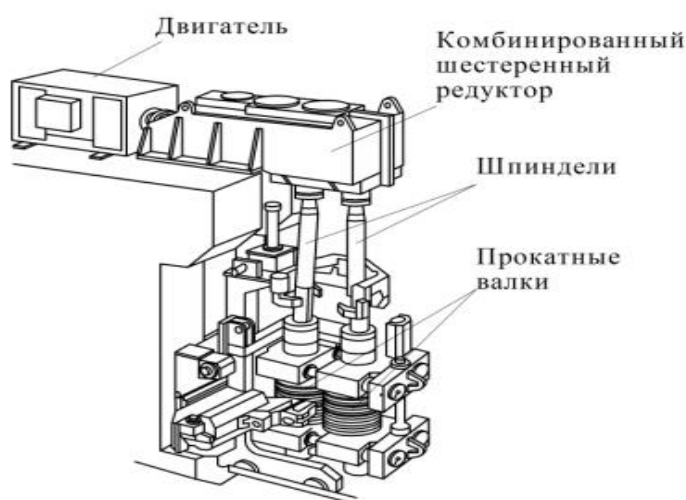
Схема расположения редуктора прокатной клетки с вертикальными валками
